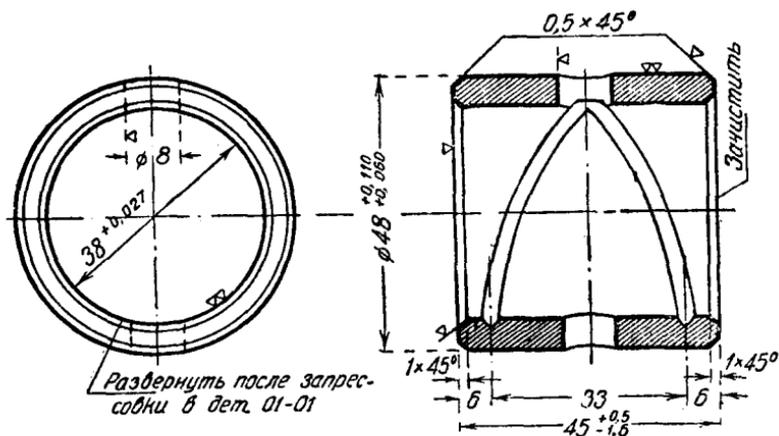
Дет. 05-08. Задняя втулка распределительного вала «Универсал»
